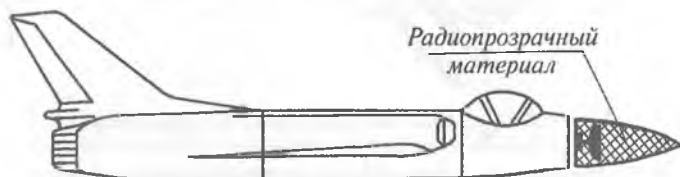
Конструктивный разъем носовой части фюзеляжа
